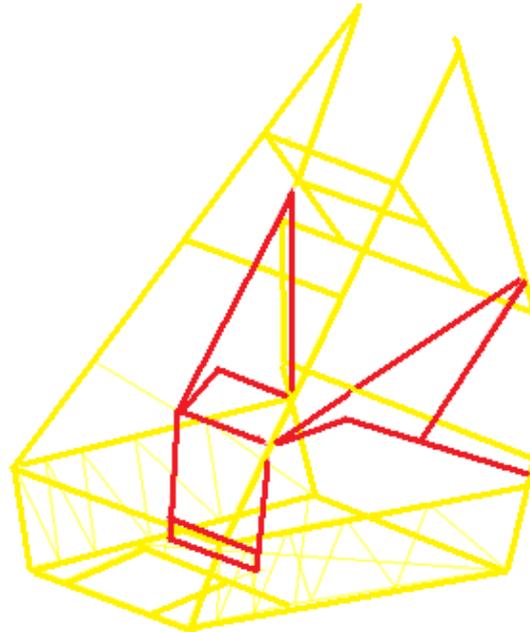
Parte trasera del chasis⁴⁰
